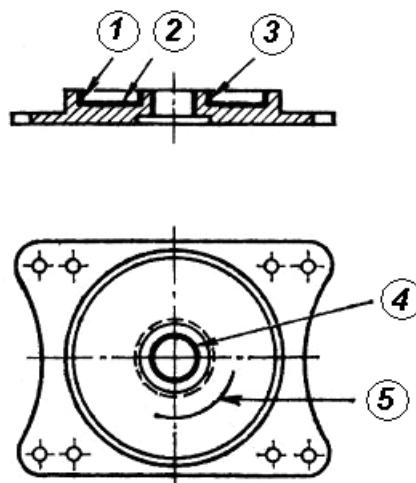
Основные дефекты подпятника, ремонтируемые сваркой или наплавкой
